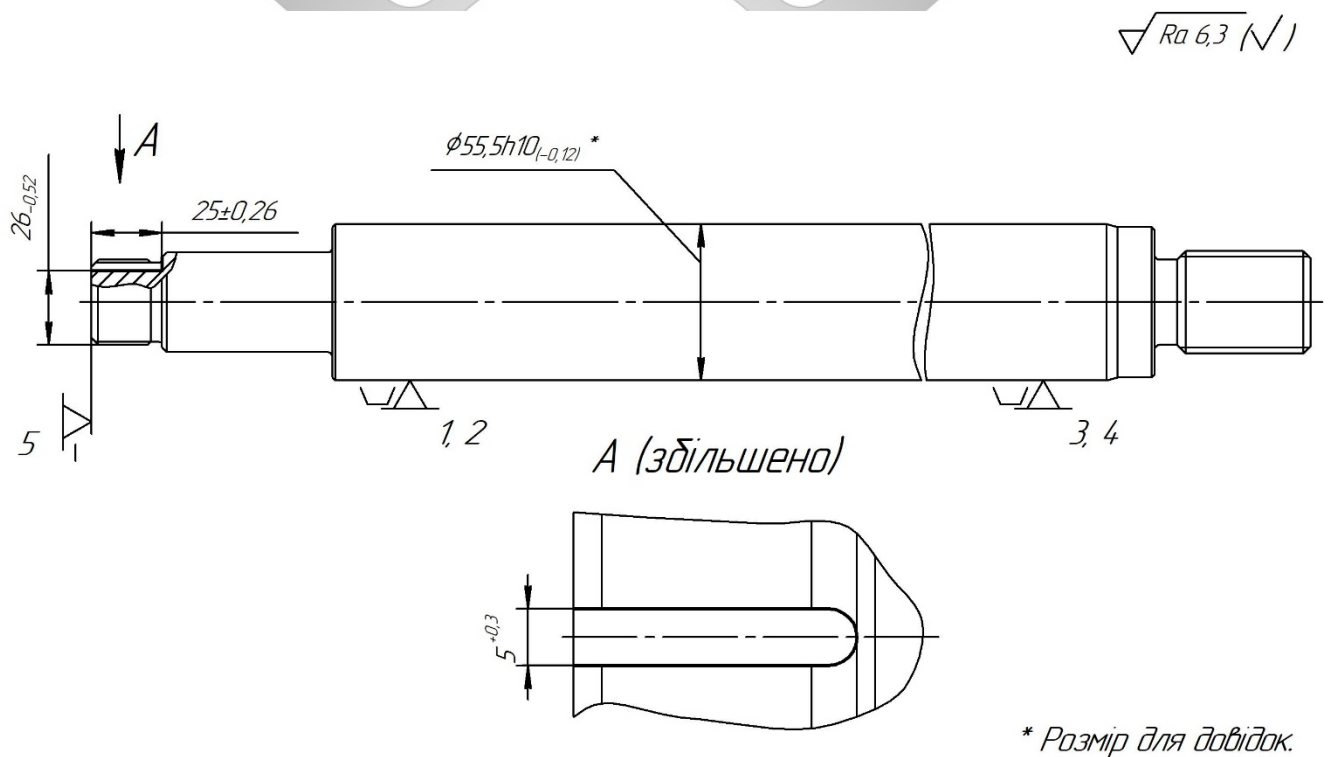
Схема базування та закріплення заготовки на операції 055 вертикально-фрезерній
